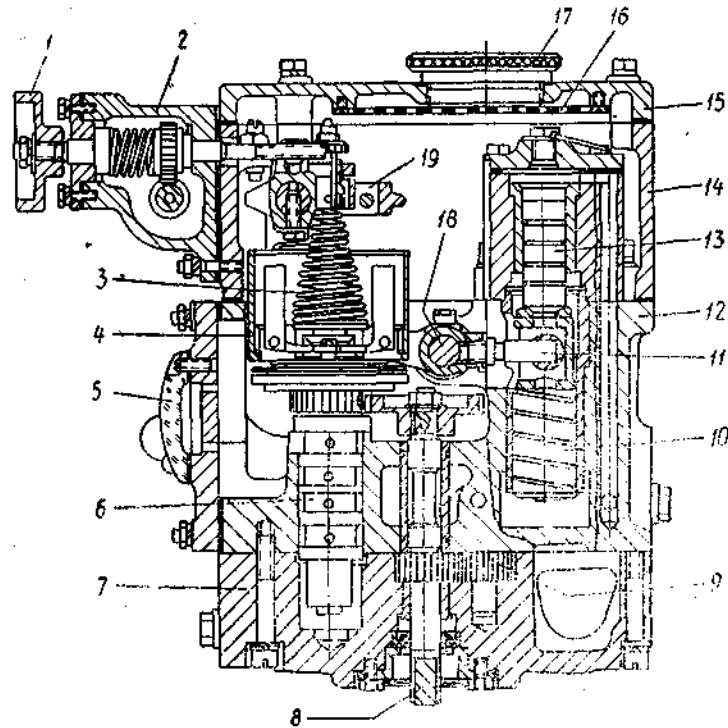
Регулятор скорости (продольный разрез): 1—рукоятка ручного управления; 2—редуктор; 3—пружина измерителя скорости; 4—измеритель скорости; 5—указатель уровня масла; 6—золотниковая часть; 7—нижний корпус; 8—приводной валик; 9—шестерня насоса; 10—управляющий поршень сервомотора; 11—палец; 12—средний корпус; 13—силовой поршень; 14—верхний корпус; 15—крышка; 16—сетка; 17—крышка горловины для заполнения регулятора маслом; 18—ось; 19—рычажная система натяга пружины измерителя скорости
